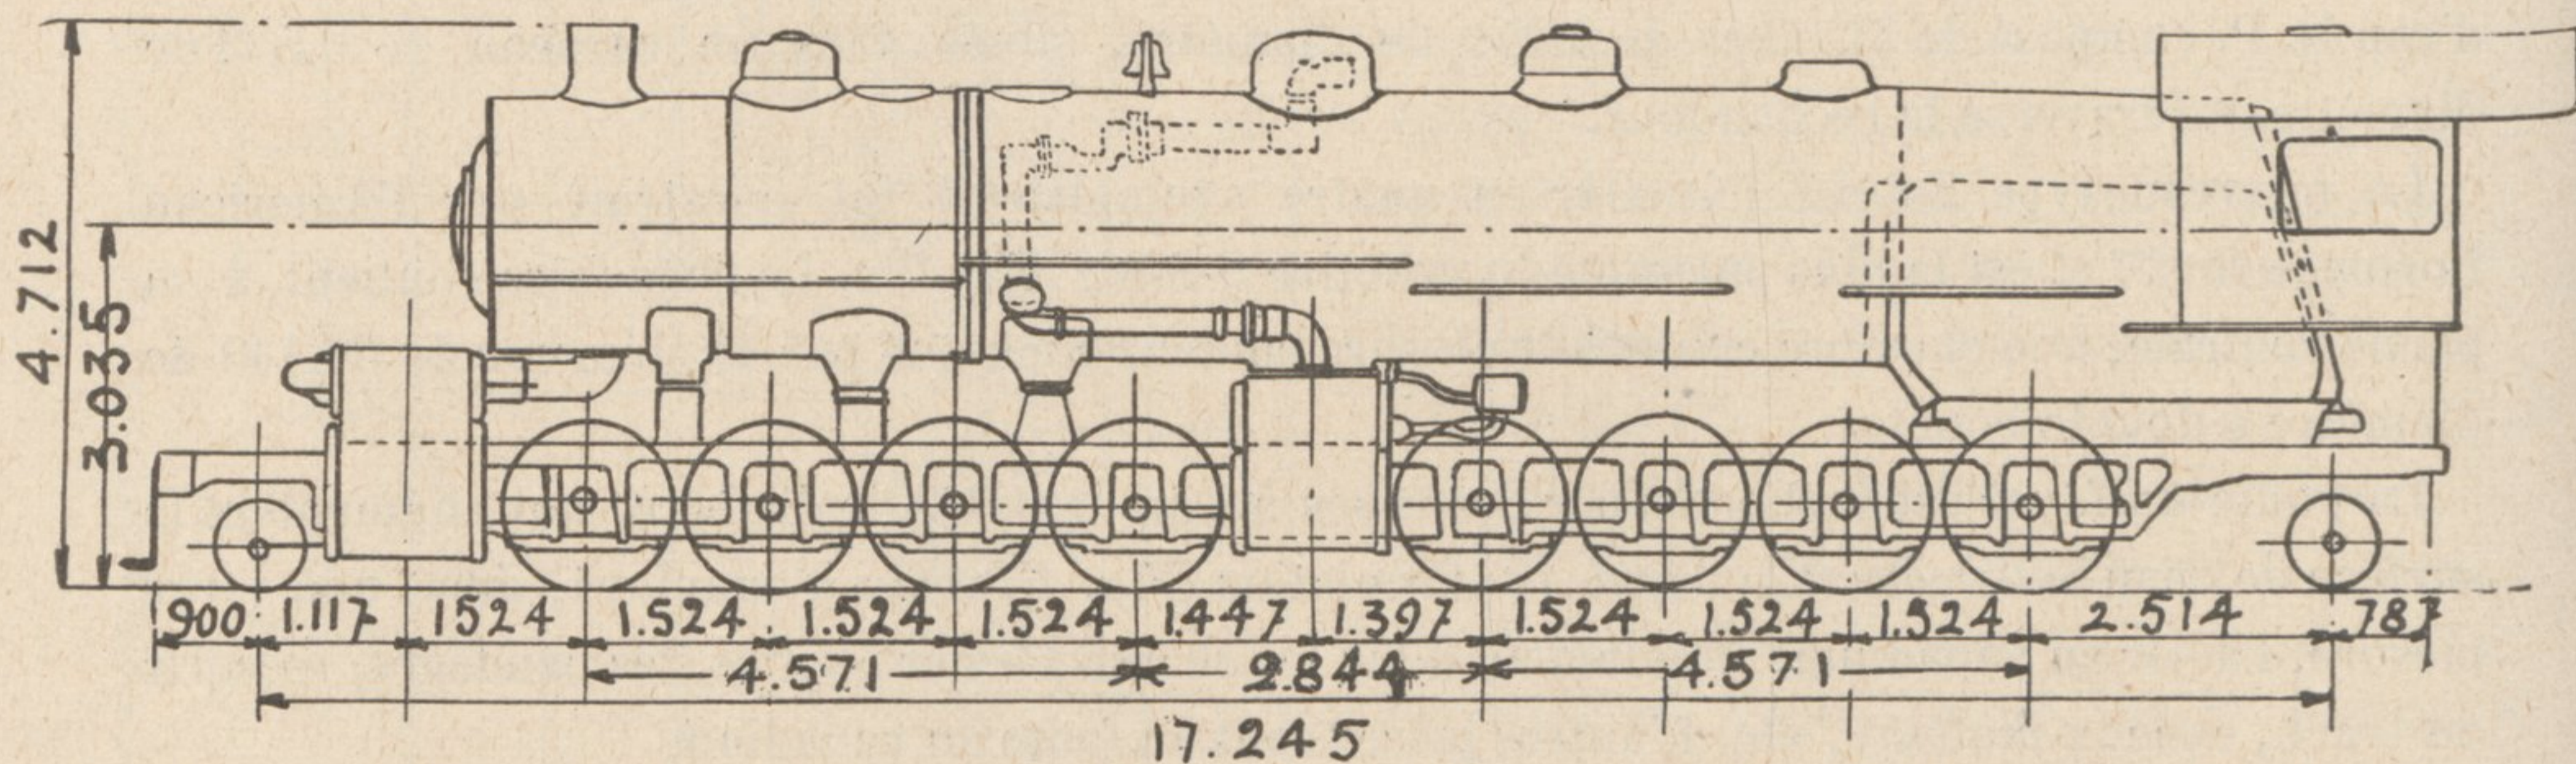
LOCOMOTIVE 2-8 + 8-2 DU ST-LOUIS IRON MOUNTAIN AND SOUTHERN R.R., CONSTRUITE PAR BALDWIN.
